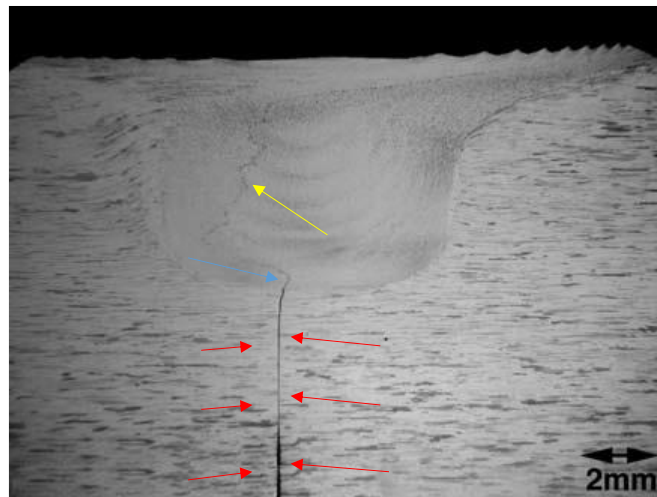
Defeito tipo “Kissing Bond” numa liga de alumínio 6082-T6 soldada por SFL.
